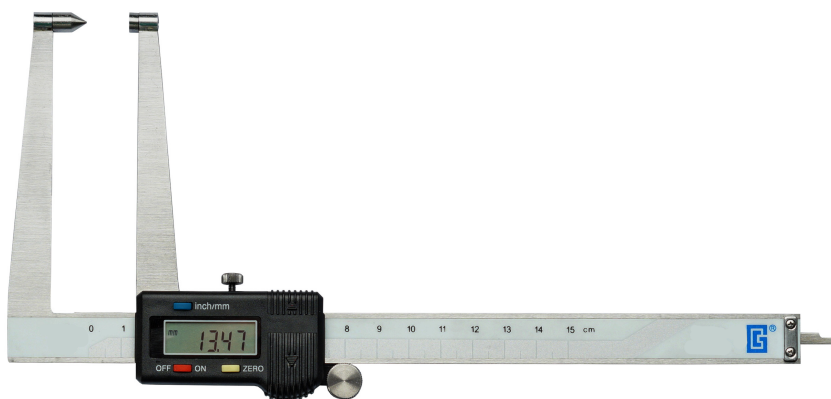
Общий вид штангенциркулей модели ШЦЦС-122
